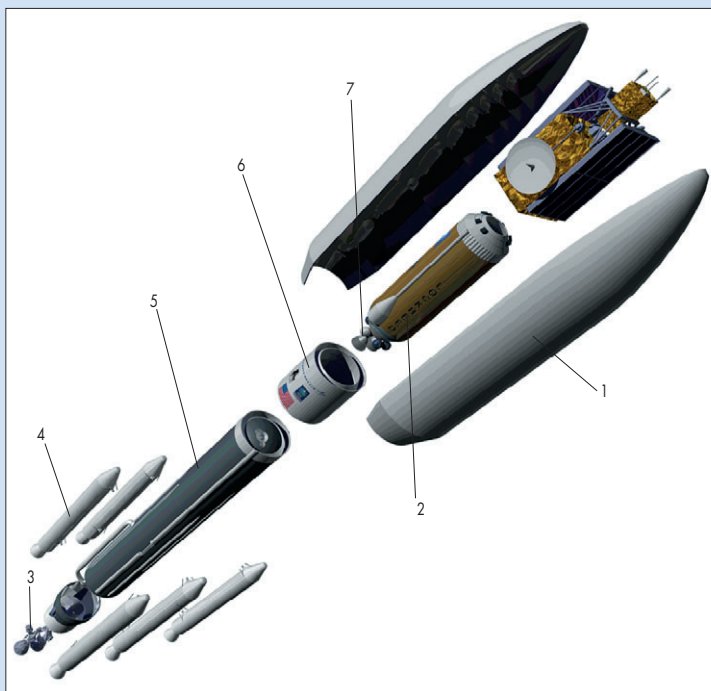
створки обтекателя; 2 – разгонный блок Centaur; 3 – двигатель РД-180; 4 – твердотопливные ускорители; 5 – общий центральный ракетный блок CCB; 6 – межступенчатый переходник; 7 – двигатели RL10. Рис. ILS
